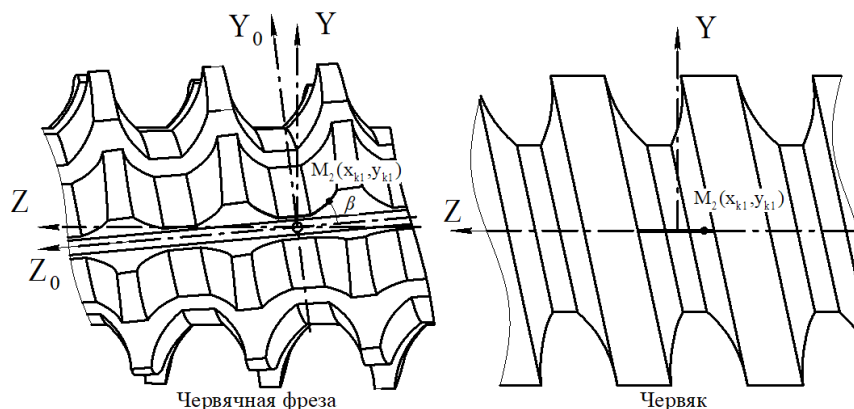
Отличия точек профилирования червяка и червячной фрезы
